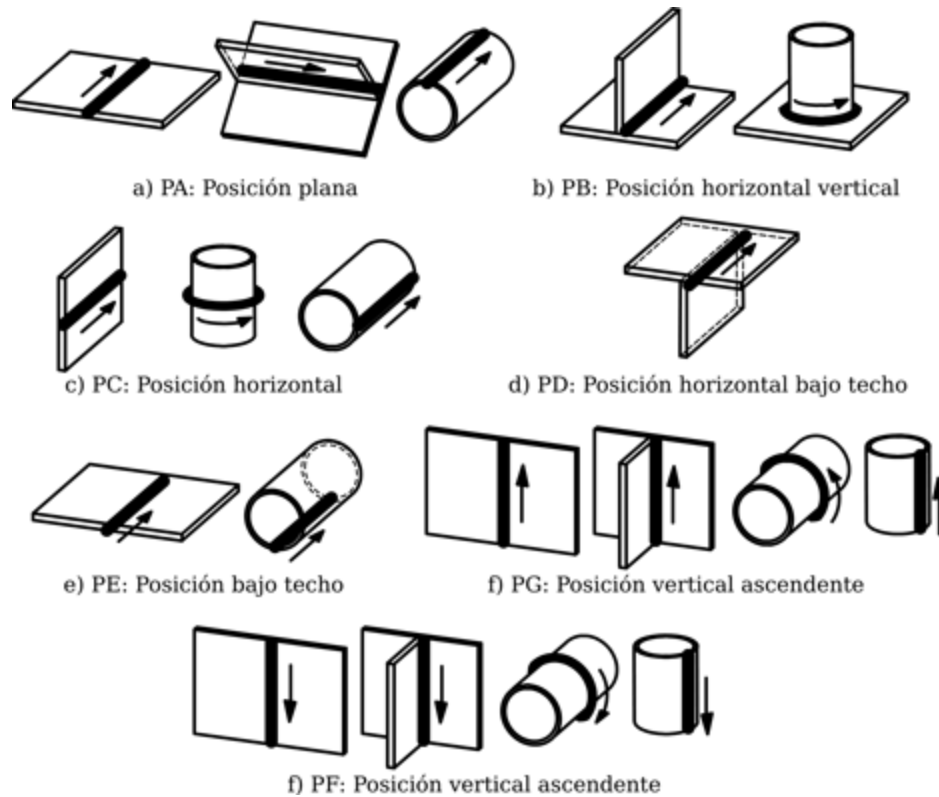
Posiciones principales de soldadura (NC-ISO 6947: 2004)
